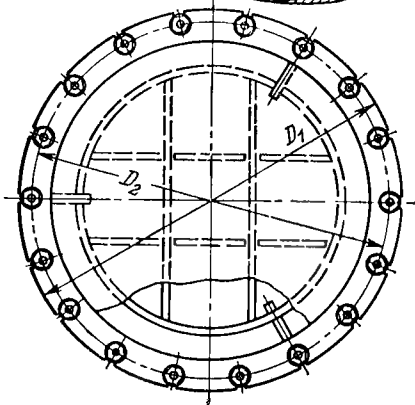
Предохранительный клапан с металлической диафрагмой.
